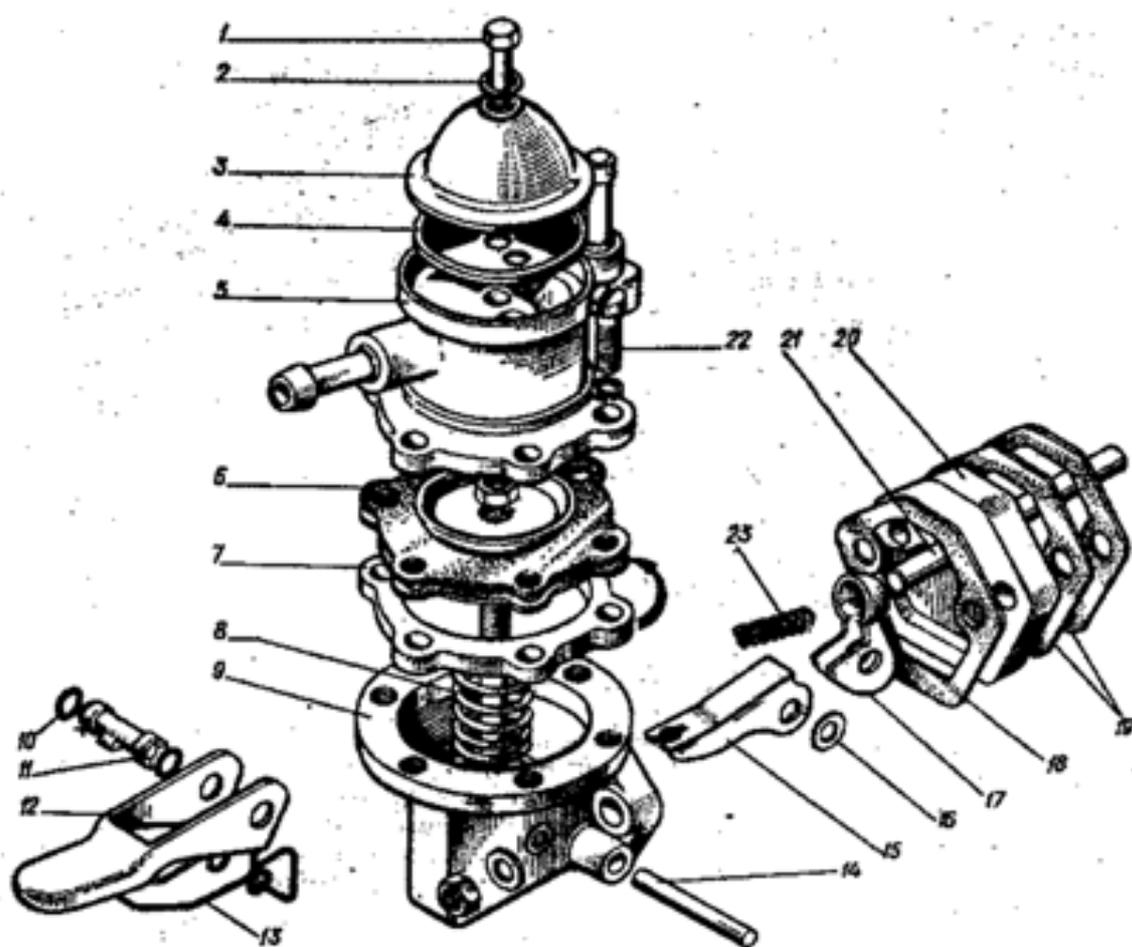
Бензиновый насос в разобранном виде: 1 - болт крышки; 2 - шайба уплотнительная; 3 - крышка; 4 - фильтр; 5 - верхний корпус; 6 - диафрагма насоса в сборе; 7 - дистанционная прокладка; 8 - центральная пружина; 9 - нижний корпус; 10 - кольцо уплотнительное; 11 - эксцентрик; 12 - рычаг; 13 - пружина рычага; 14 - ось рычага и балансира; 15 - балансир; 16 - шайба рычага заполнителя; 17 - рычаг привода; 18 - прокладка; 19 - прокладки регулировочные; 20 - проставка; 21 - штанга; 22 - винт с пружинной шайбой; 23 - возвратная пружина рычага
